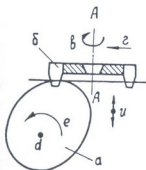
Схема нарезания некруглого цилиндрического колеса с арочными зубьями
